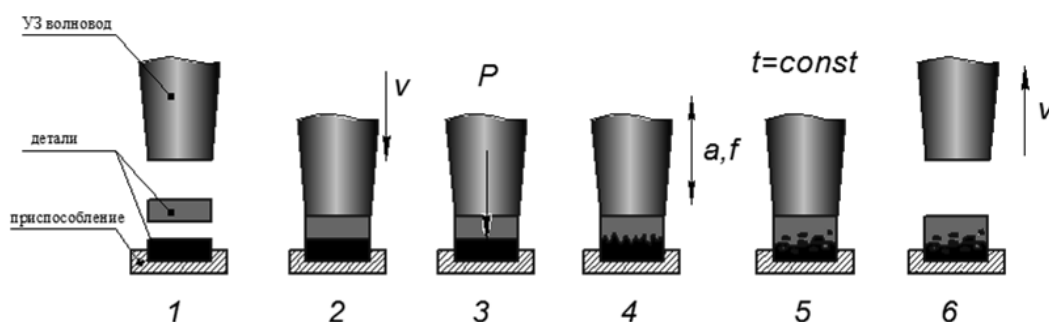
Схема цикла ультразвуковой сварки
